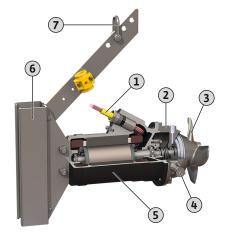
Vista geral do mecanismo agitador de motor submersível
